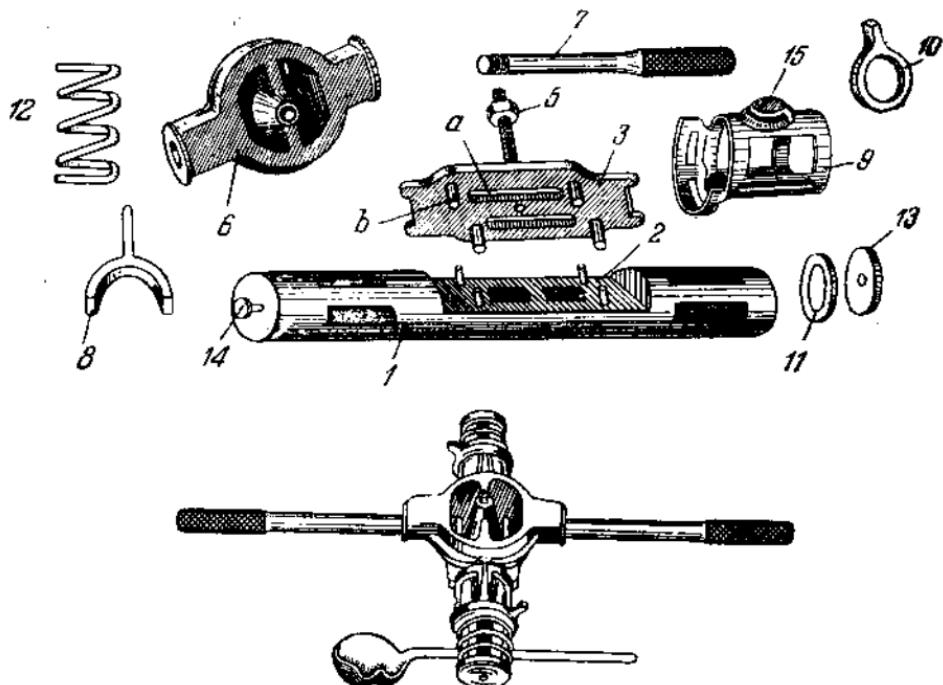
Прибор «Хемпи-Купер Н-40» для галваники коренных подшипников.
